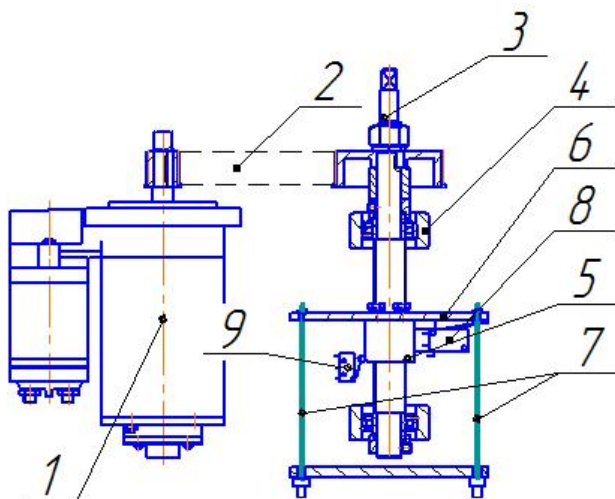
Структурная схема ЭМПСТС АТС: 1 – электродвигатель; 2 – передача зубчатый ремень (ременная передача); 3 – винт передачи винт-гайка; 4 – подшипник; 5 – гайка передачи винт-гайка; 6 – коромысло; 7 – натяжные тросы тормозных механизмов; 8 – выключатель верхний; 9 – выключатель нижний
